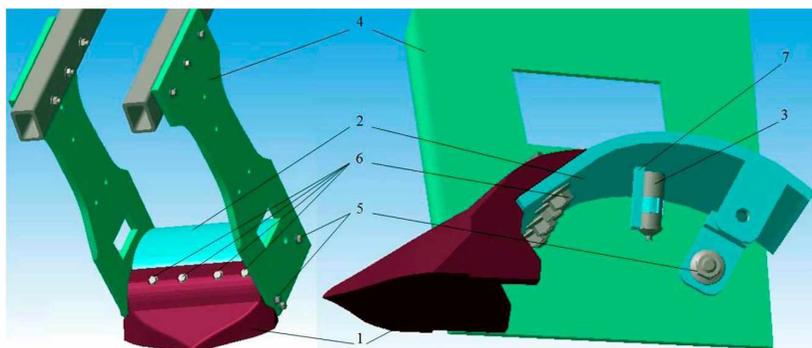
Модернизированная культиваторная лапа устройства для создания минерализованной полосы противопожарного назначения: 1 – культиваторная лапа; 2 – сферический козырек; 3 – форсунка мелкодисперсного распыления; 4 – стойки
